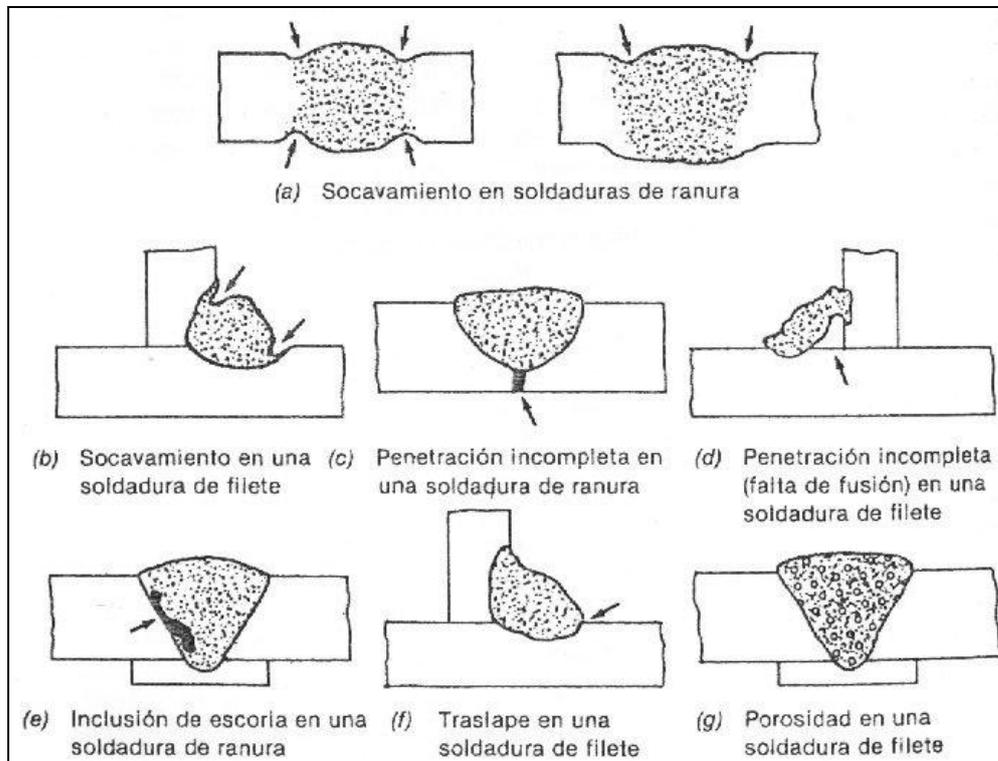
Diferentes tipos de defectos en las soldaduras
